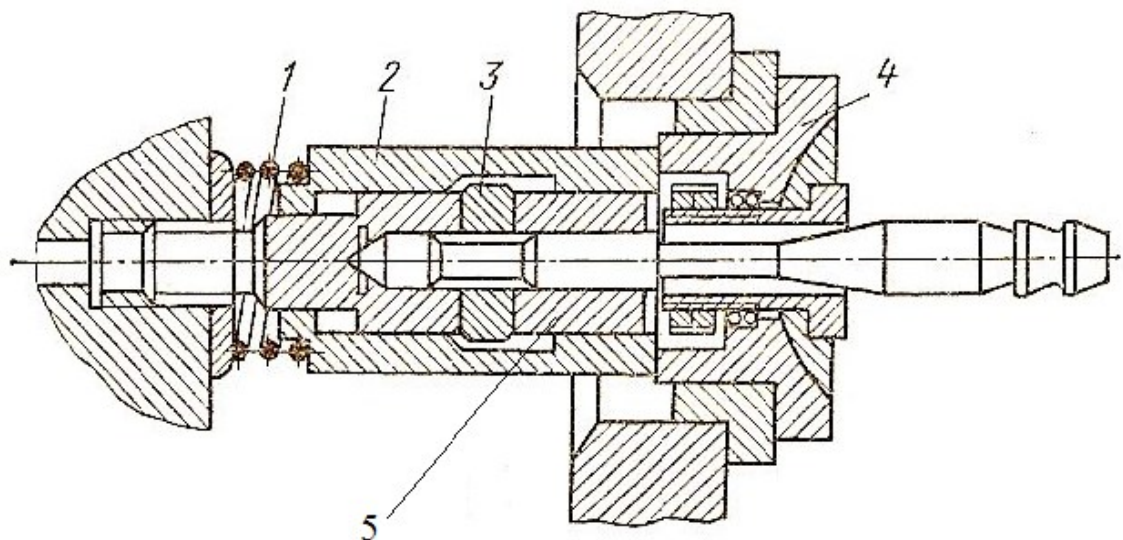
Швидкозмінний патрон для протяжок
